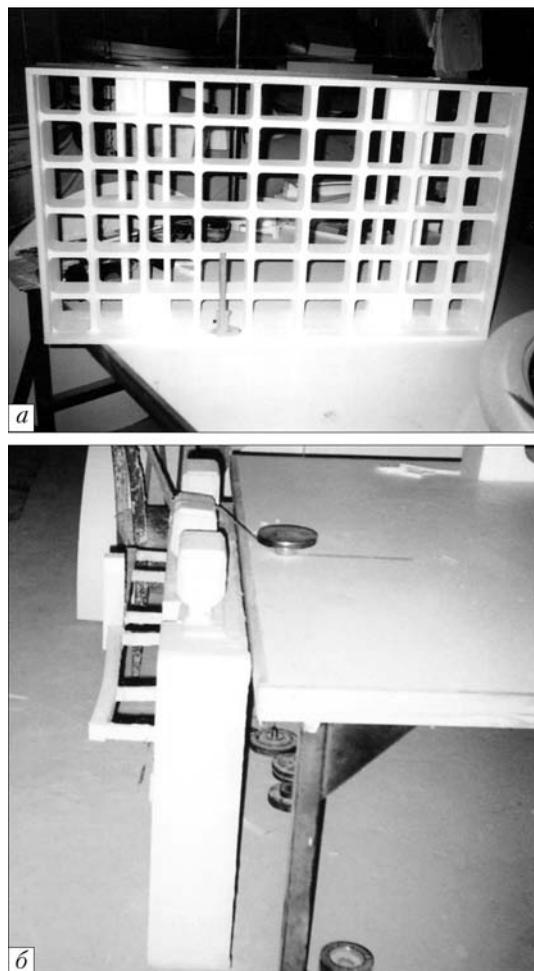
Модели заготовки поддона (а) и заготовки с литниково-питающей системой (б)
